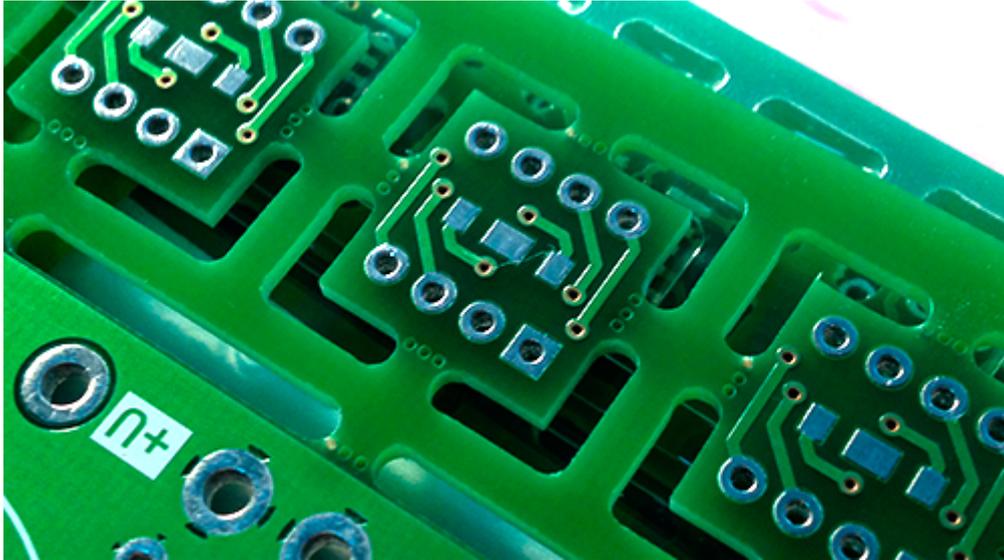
Фрезеровка контура платы и перфорация для разделения
